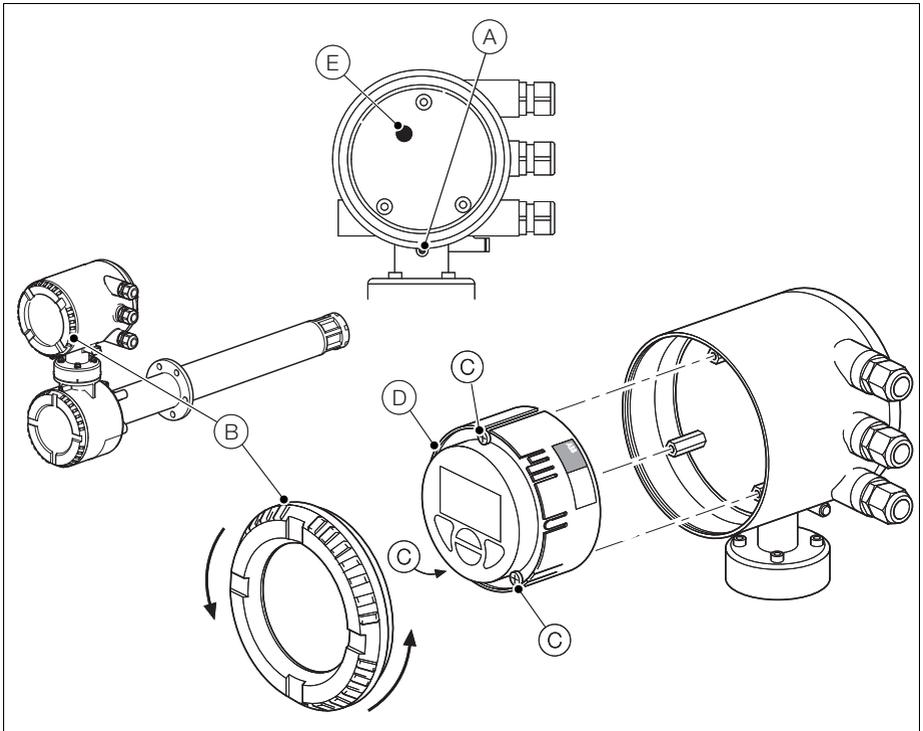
Integrierter Messumformer – Austausch der internen Sicherung
